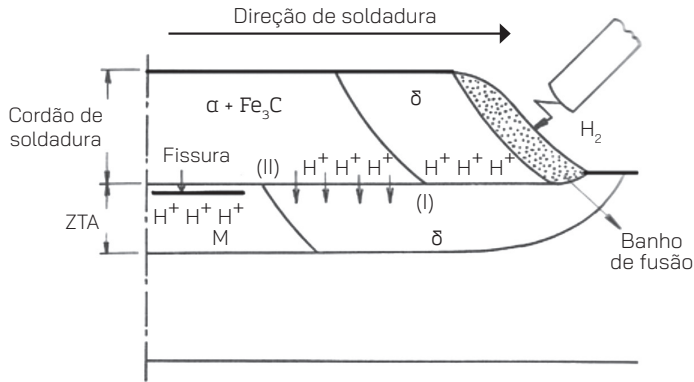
Esquema de fragilização por hidrogênio no processo de soldadura. O pré-aquecimento diminui a taxa de arrefecimento, após soldadura, permitindo a libertação do hidrogênio por difusão².
